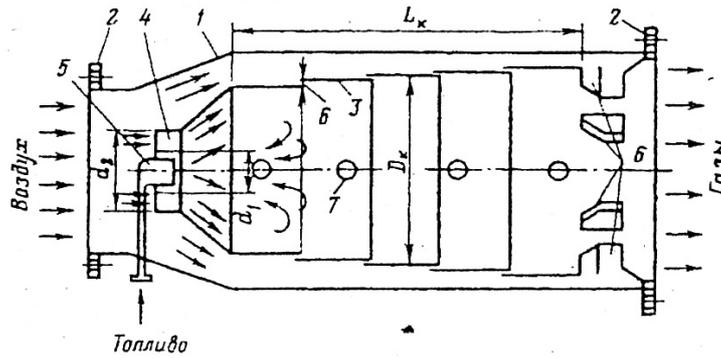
2. Схема камеры сгорания: 1 - корпус; 2 - фланцы; 3 - жаровая труба; 4 - регистр; 5 - распылитель (горелка); б — смеситель; 7 — смотровые отверстия
